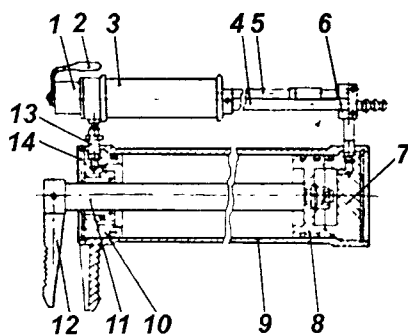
Бортрозширювач ручний з пневматичним приводом
